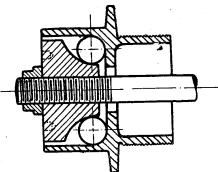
Exemple de Roulement à cone et à cuvette.
